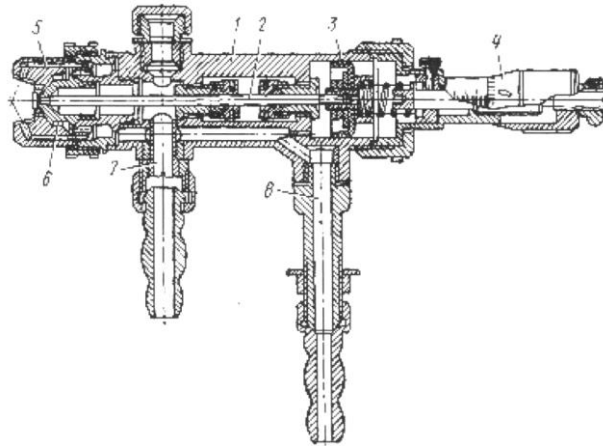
Пневматичний розпилювач з автоматичним керуванням моделі КРВ-2: 1 - корпус; 2 - голка; 3 - клапан; 4 - регулятор витрати лаку; 5 - головка; 6 - кільцевий канал; 7 - канал подавання лаку; 8 - канал подавання повітря
